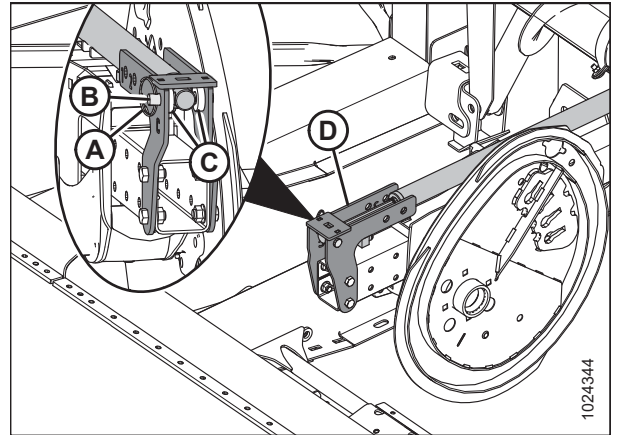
Центральний важіль мотовила в передньому положенні
